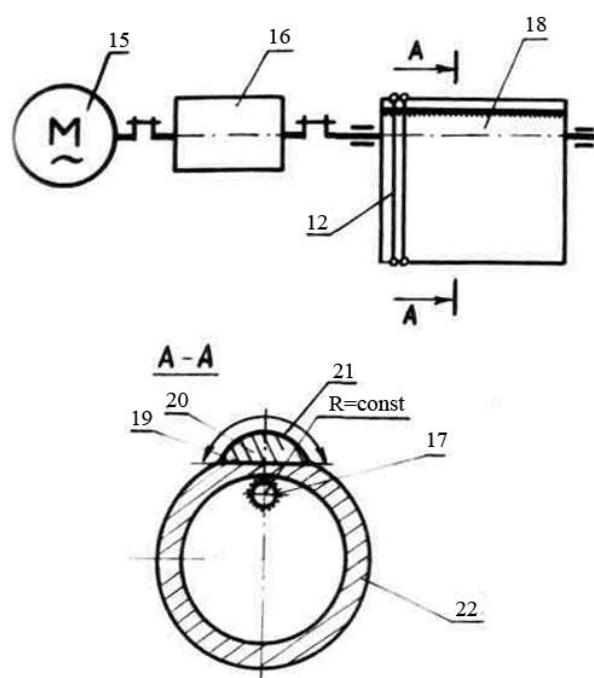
Устройство реверсивного привода кормораздатчика с дозированием в трубе
